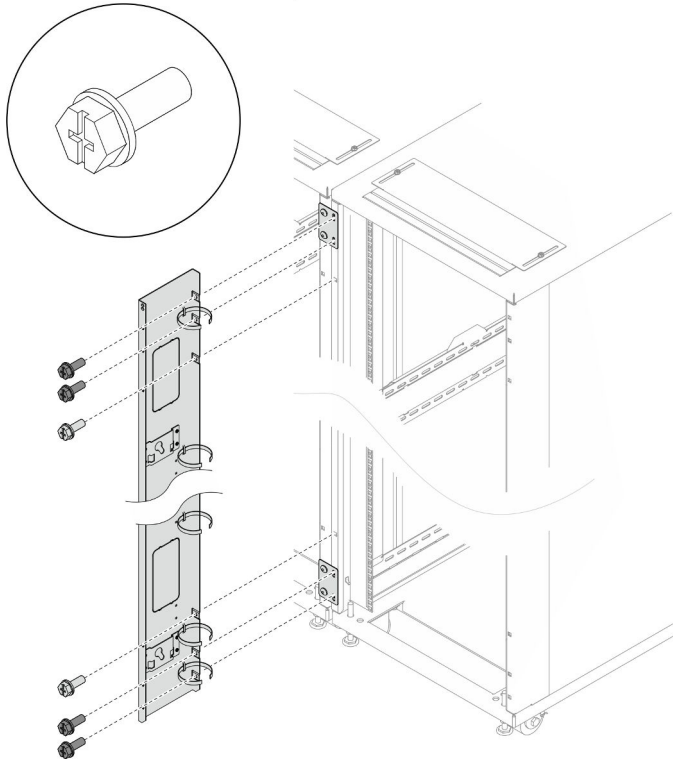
Installation d'un panneau d'extension (avec kit de juxtaposition)
